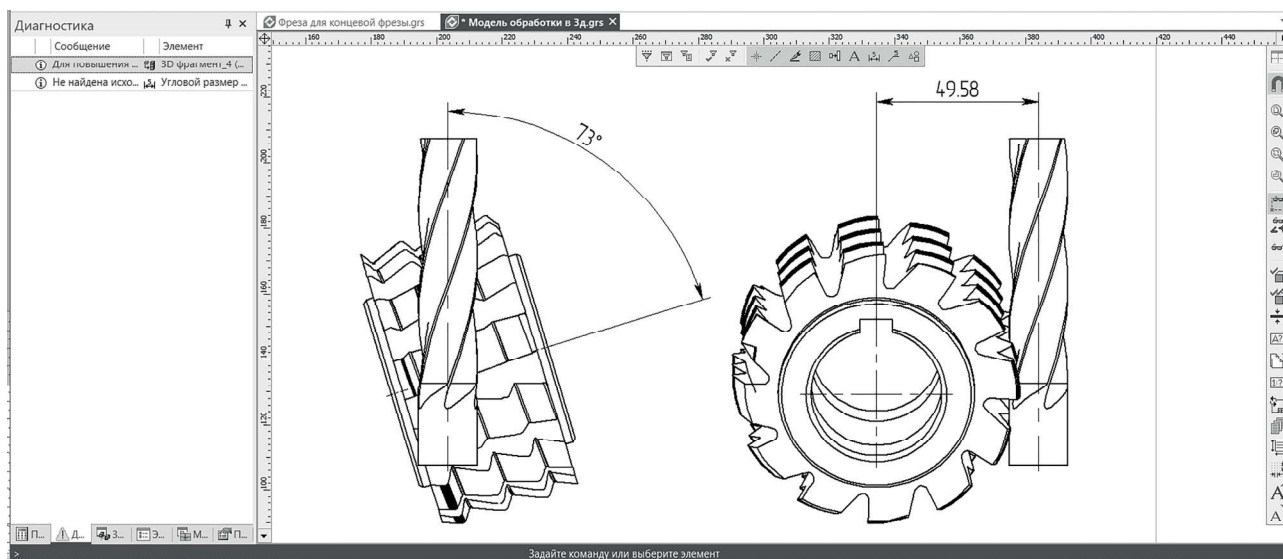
Параметры установки червячной фрезой относительно обрабатываемой детали в T-flex CAD
